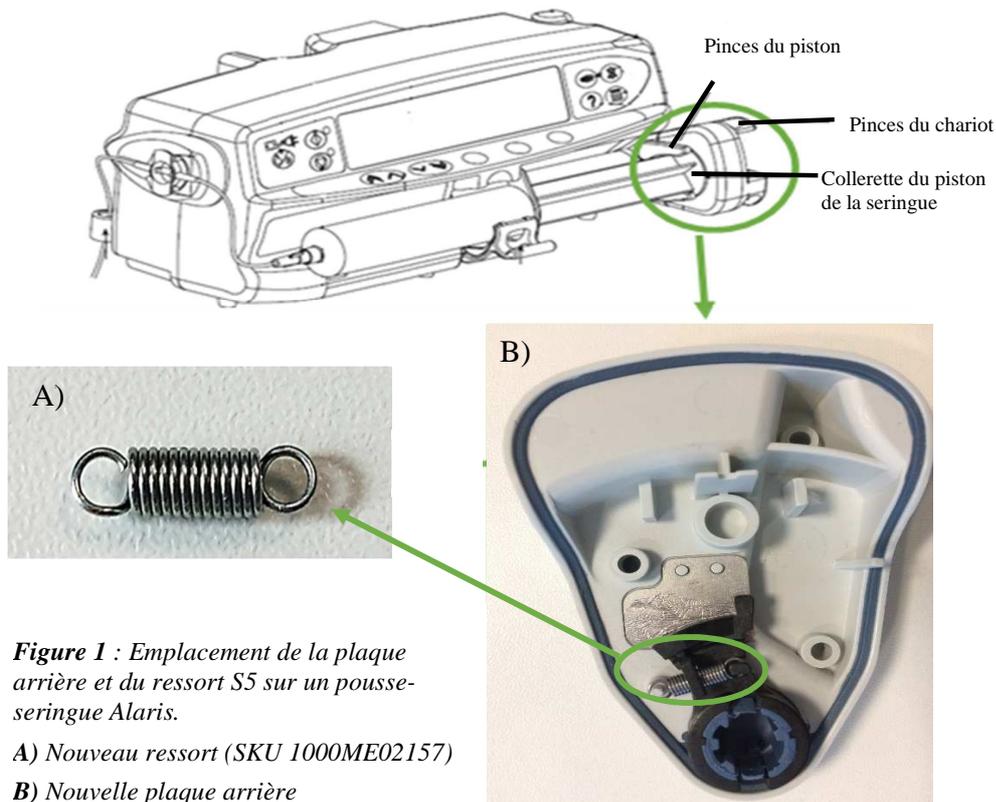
Emplacement de la plaque arrière et du ressort S5 sur un pousse-seringue Alaris.
